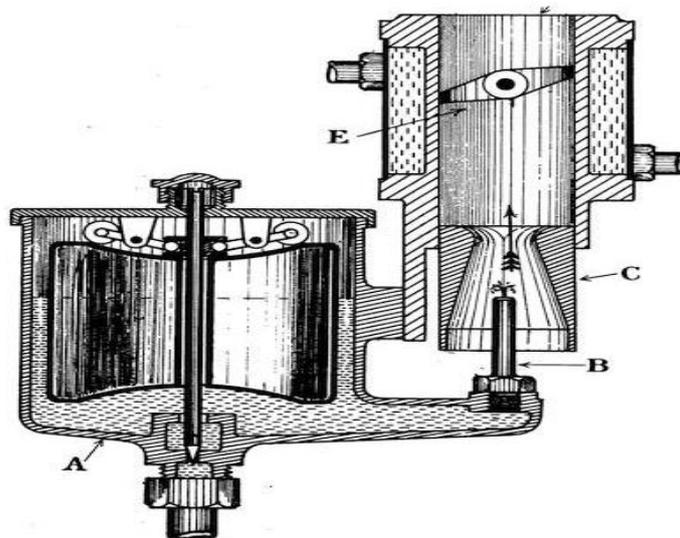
Dessin en coupe d'un carburateur de type Jet
